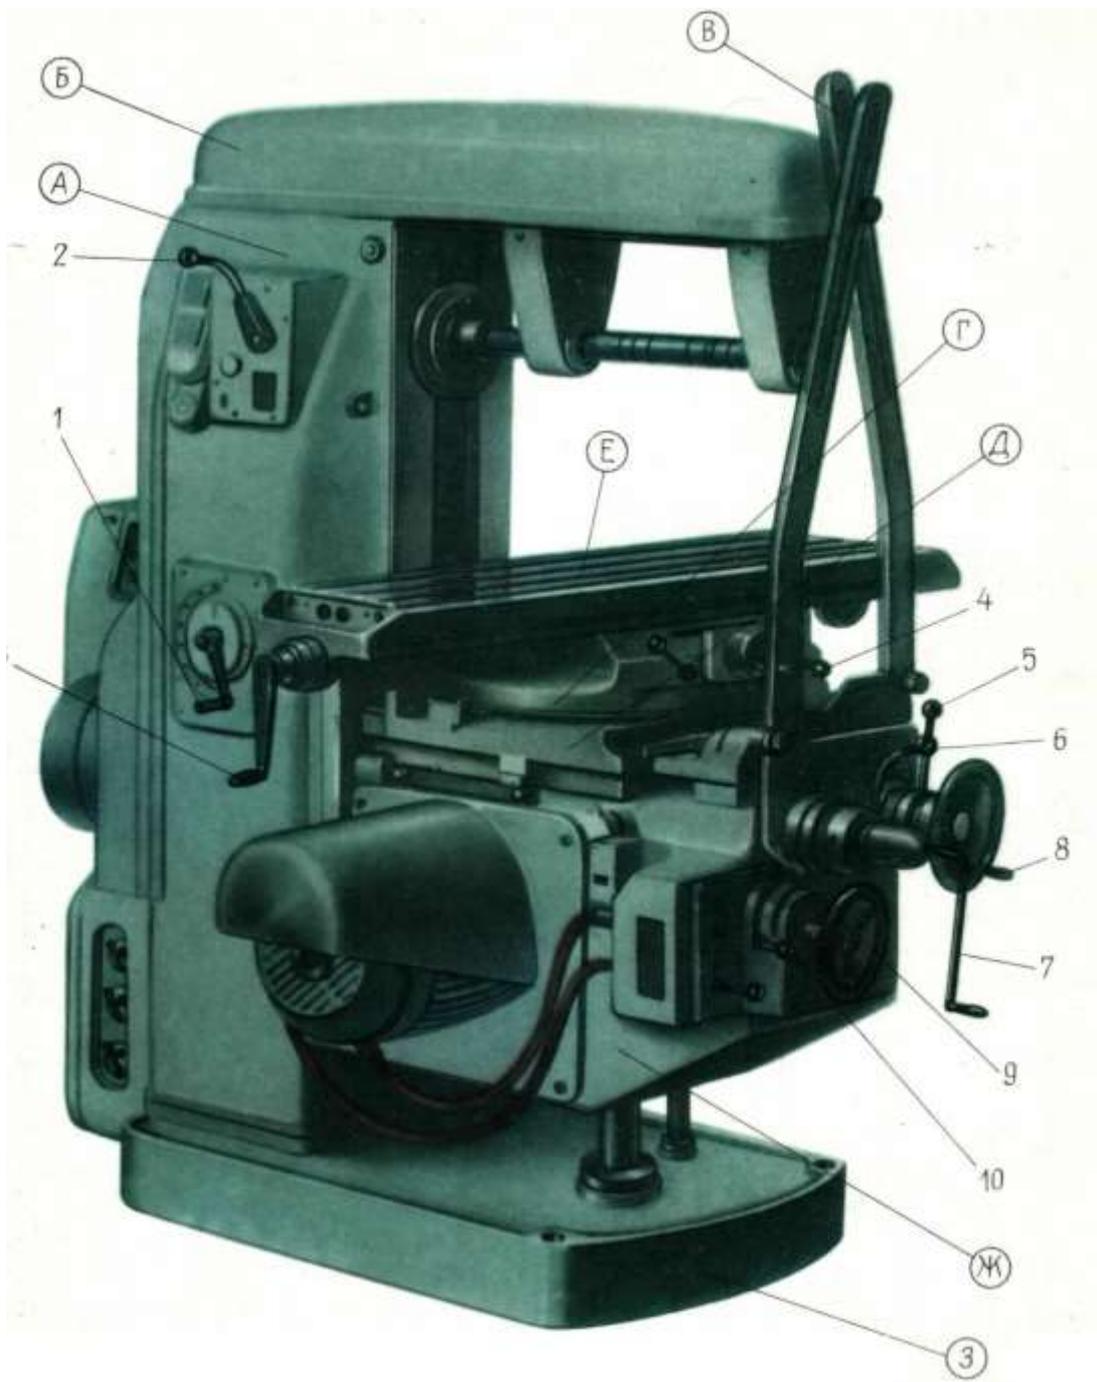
Общий вид универсально-фрезерного станка модели 6Н81
